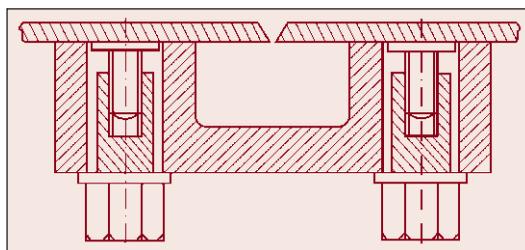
Схема сборочного приспособления с приваренными к листам шпильками
